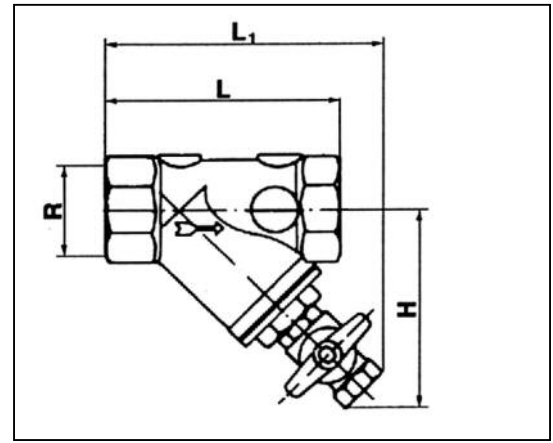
Габаритные размеры фильтров сетчатых типа Y222P.
